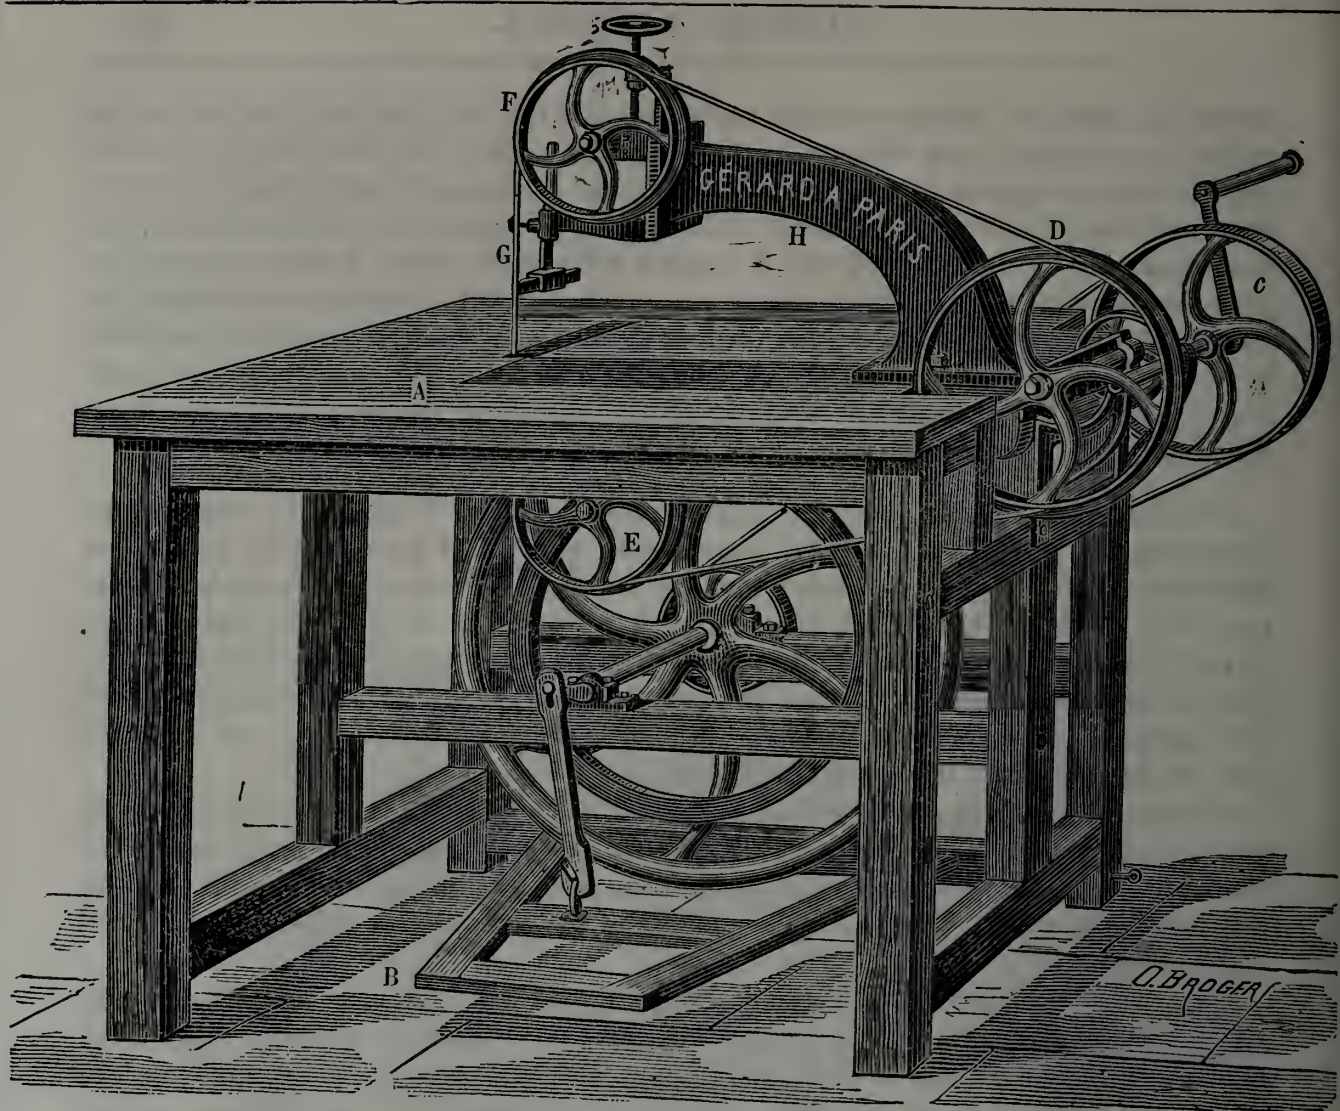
Machine à couper les tissus, de M. Gérard.
